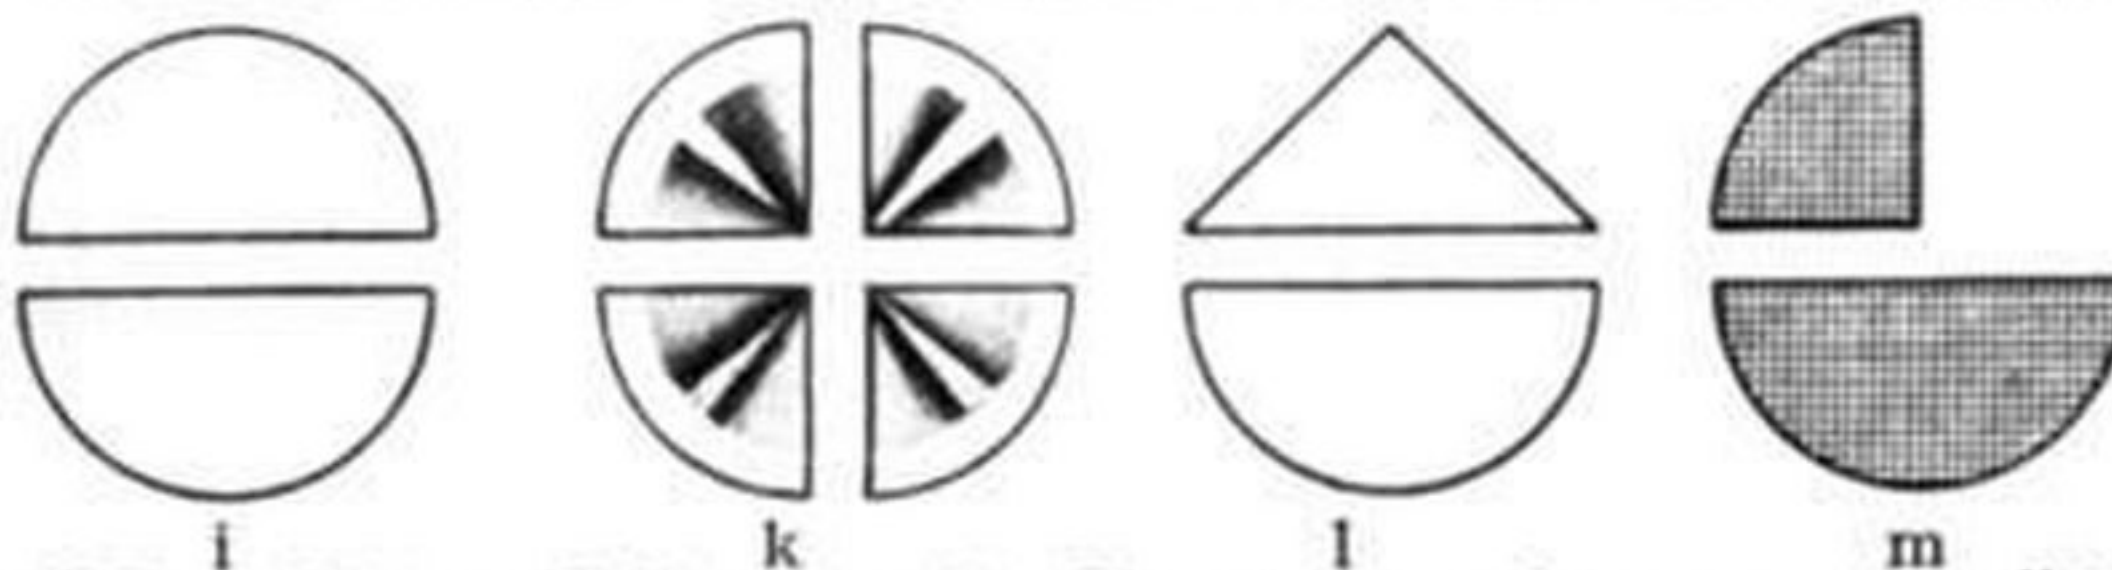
Untere Seite von vier Fassungswerkzeugen; i = Öffner, k = Verdrücker, l = Erweiterer und m = Tiefenfräser
